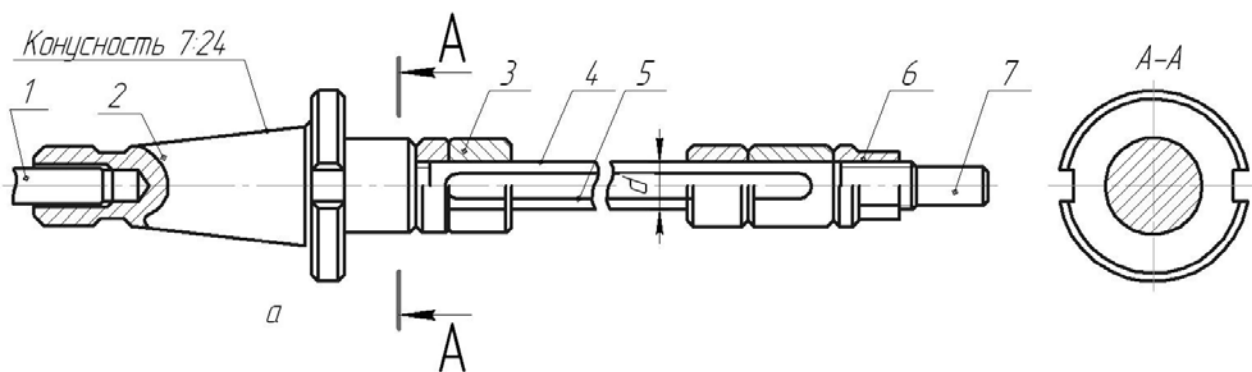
Центровая оправка с направляющей цапфой
